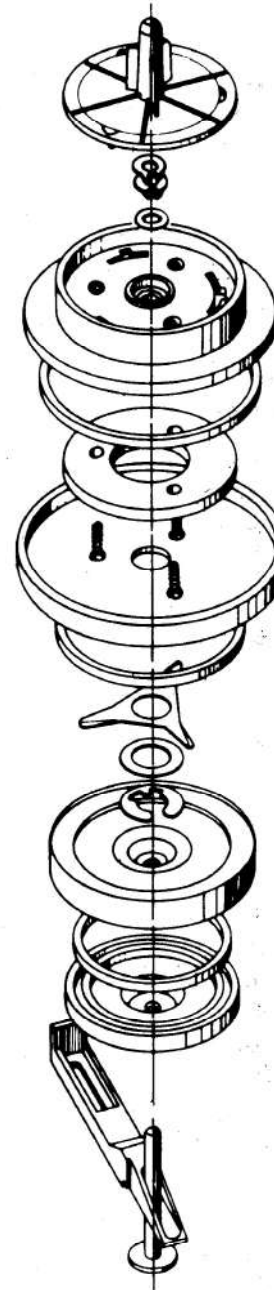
Explodierte Darstellung des rechten Wickeltellers
